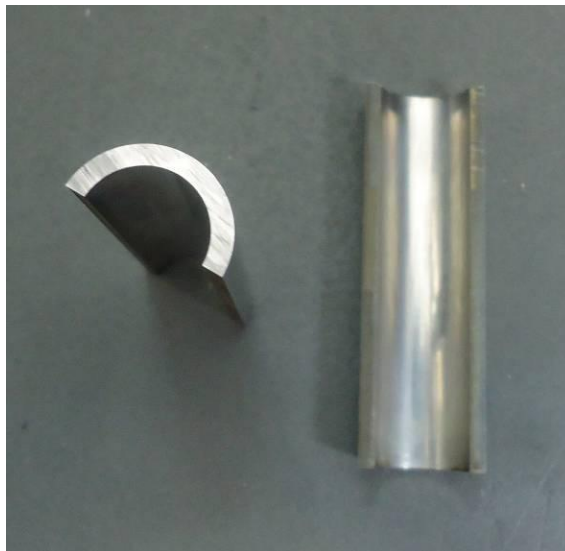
Corpo de prova pronto para ser submetido ao processo de soldagem TIG autógeno manual.
